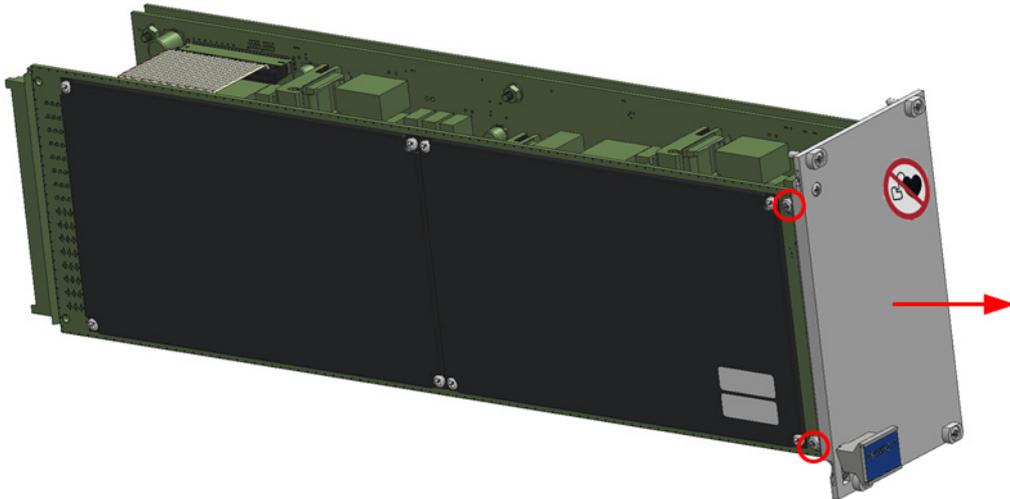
Lösen der Schrauben und Entfernen der ES4452.1 Frontplatte
